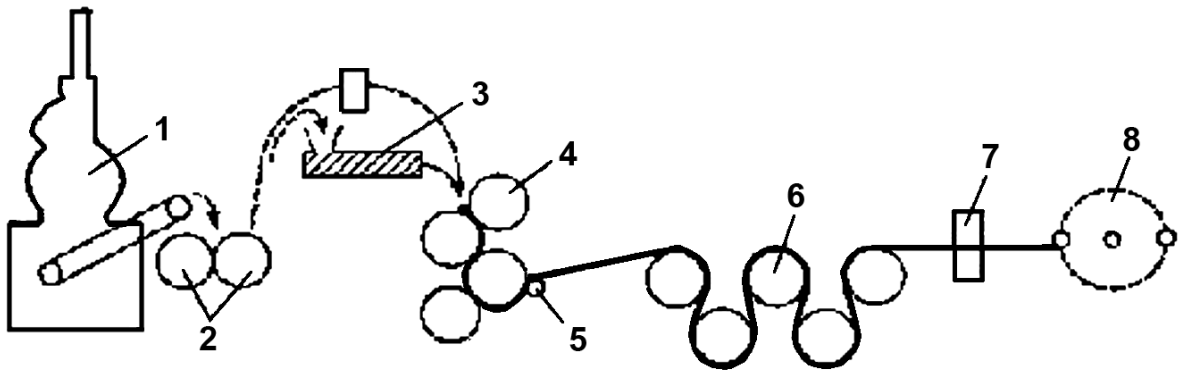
Технологічна схема одержання плівки з термопластичного матеріалу методом каландрування. 1 – змішувач; 2 – валки; 3 – шприц-машина; 4 – похилий Z – подібний каландр; 5 – відбірний ролик; 6 – охолоджуючі валки; 7 – товщиномір; 8 – приймальний пристрій
